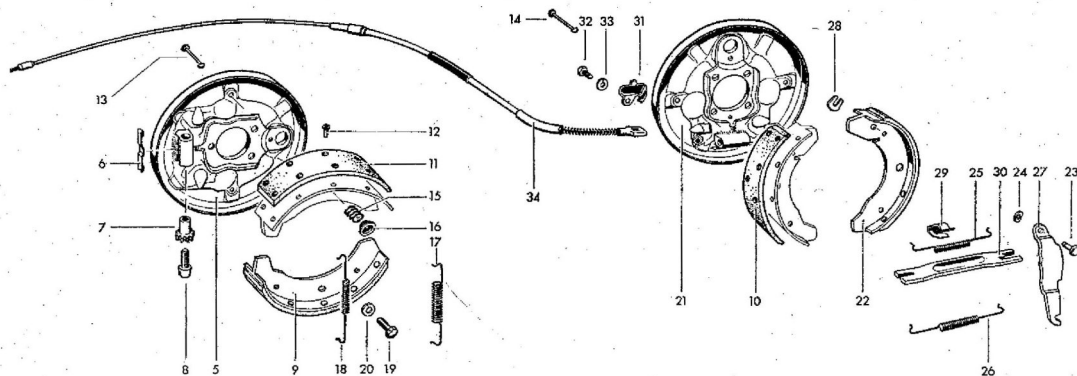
Montagebild der zerlegten Öldruckbremse (Standard-Ausführung)
